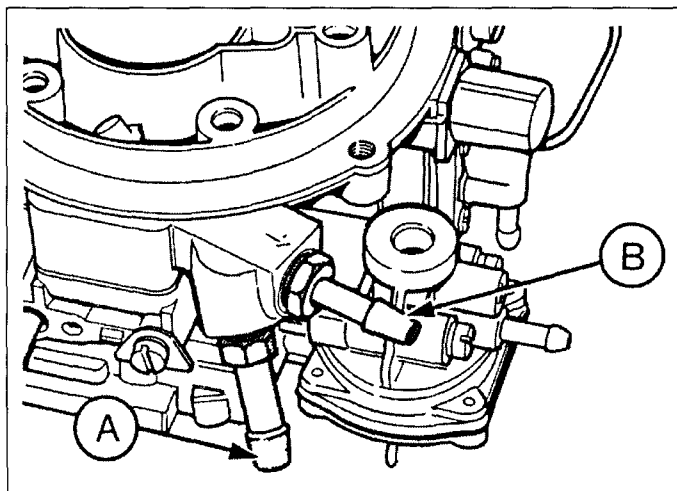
,а. Топливные штуцеры карбюратора (26/28, 28/30 -двигатели 1.1 л)
